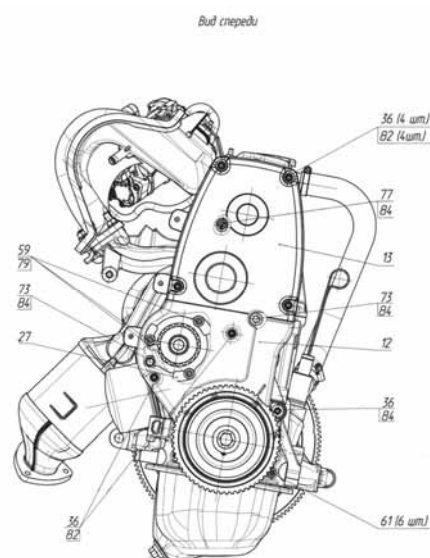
Двигатель ВАЗ – 21116 - вид спереди
